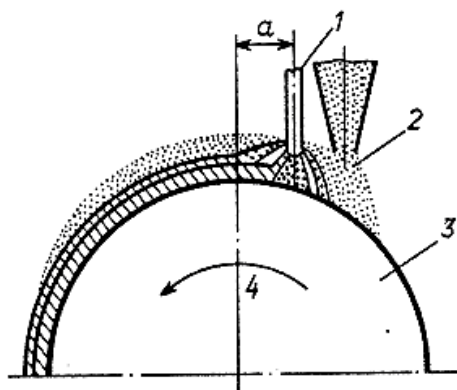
Смещение (a) электрода при наплавке цилиндрических деталей:
